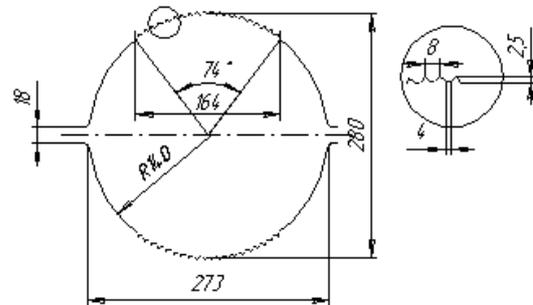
Круглый калибр для прокатки прутков Ø265мм
